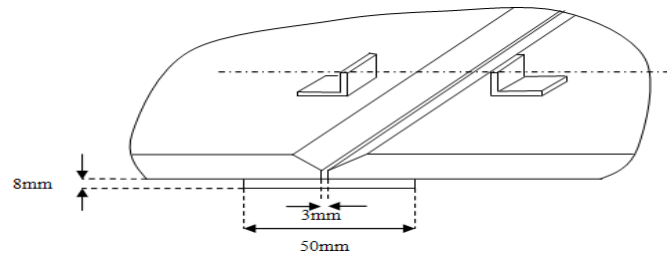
Assemblage bout à bout (tôles marginales)
